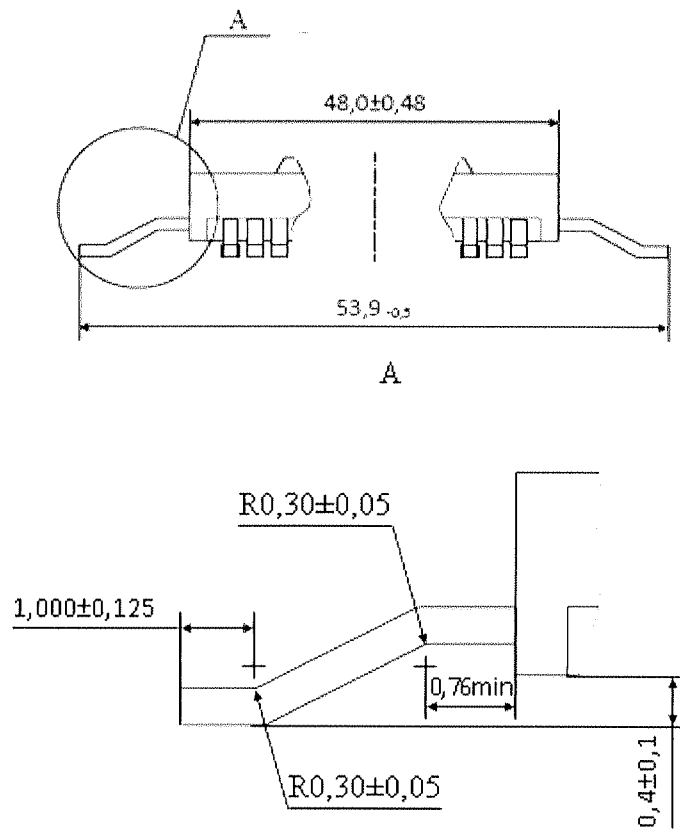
Рекомендуемый вид формовки и обрезки выводов микросхем 5529ТР104
